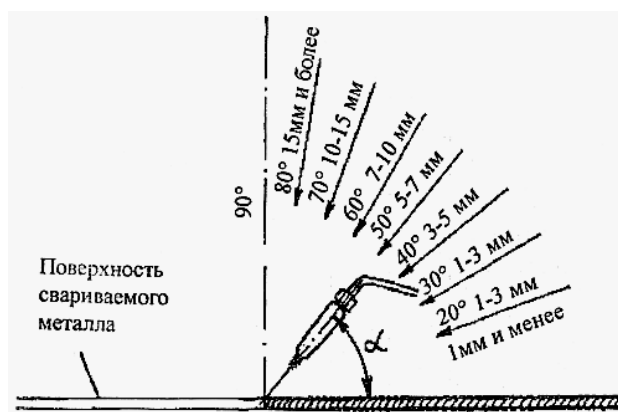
Углы наклона мундштука горелки при сварке стали различной толщины
